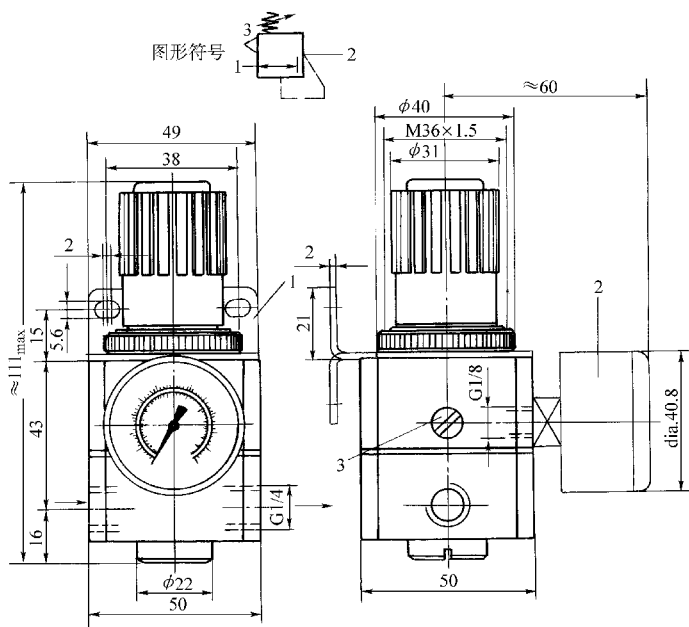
LRP-1/4 型精密低压减压阀外形尺寸
